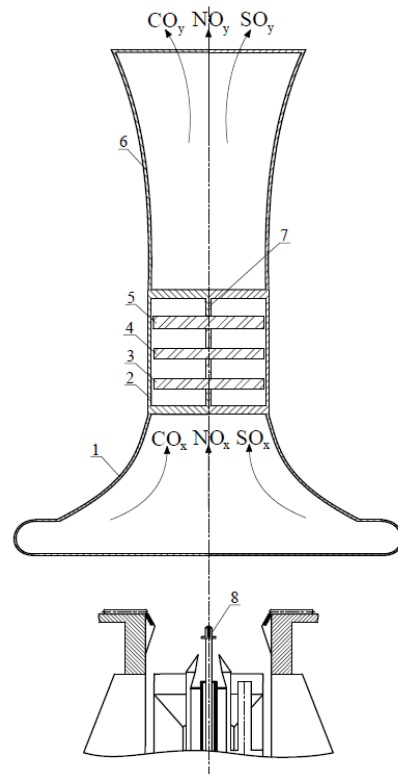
Схема динамического каталитического дожигателя: 1 — конфузор; 2 — корпус дожигателя; 3, 4, 5 — рабочие колеса; 6 — диффузор; 7 — вал рабочих колес; 8 — горелочное устройство котлоагрегата
